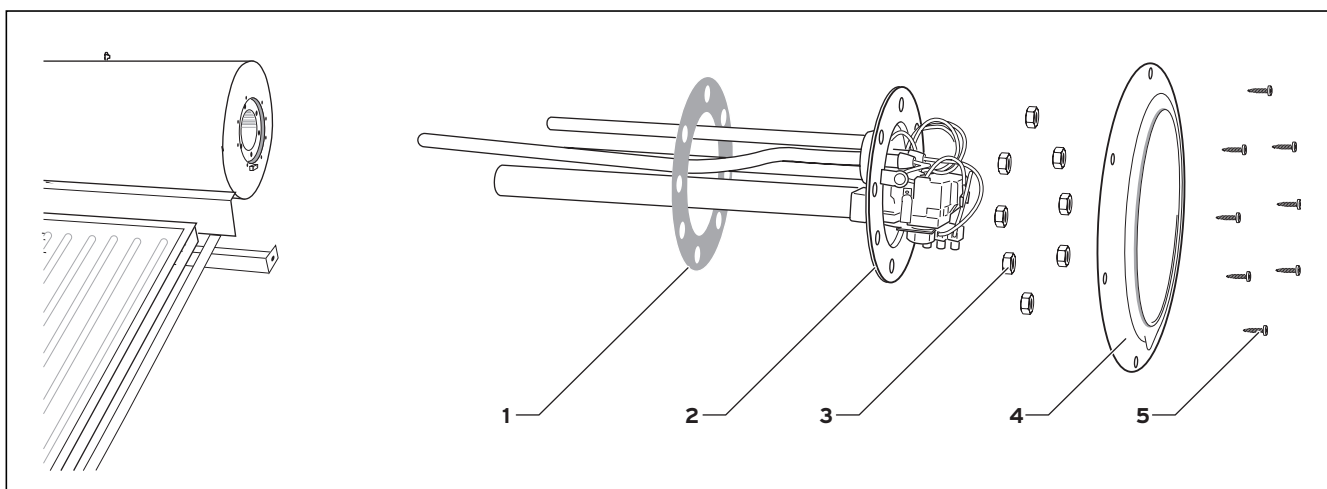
Montaggio del riscaldatore elettrico a immersione
